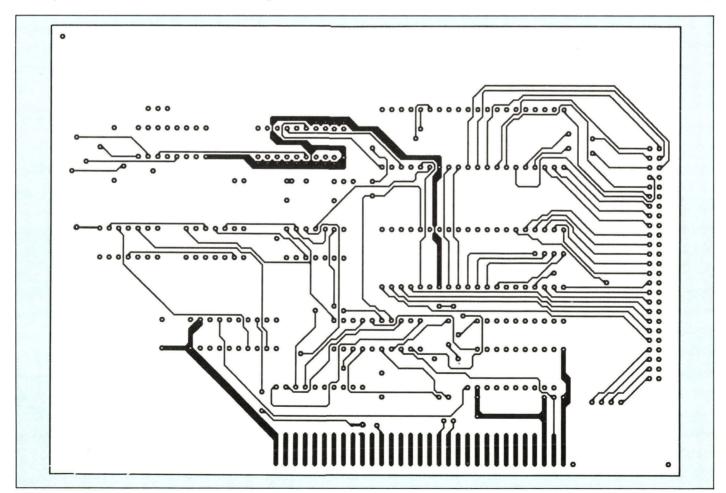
Circuit imprimé vu côté soudures.
